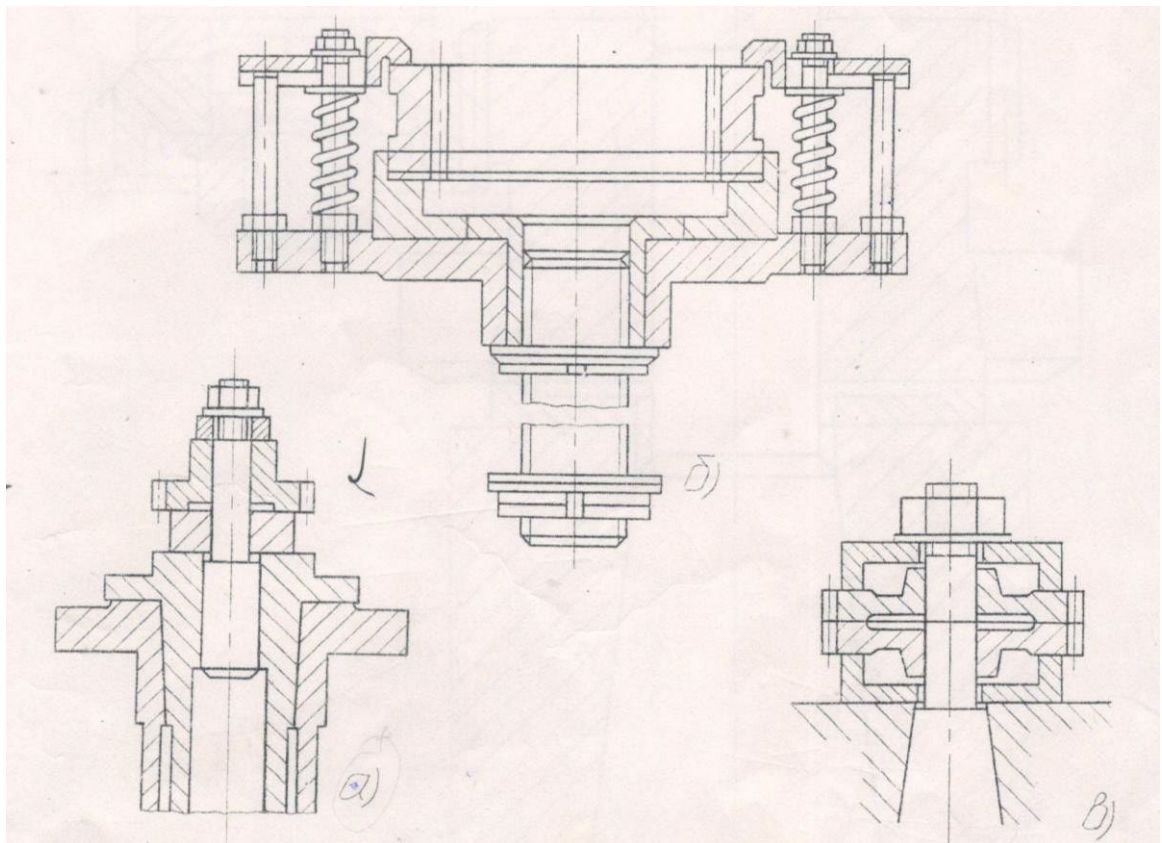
Схемы установки и крепления заготовки при зубодолблении: а – зубчатого колеса; б – венца; в – пакета колес.
